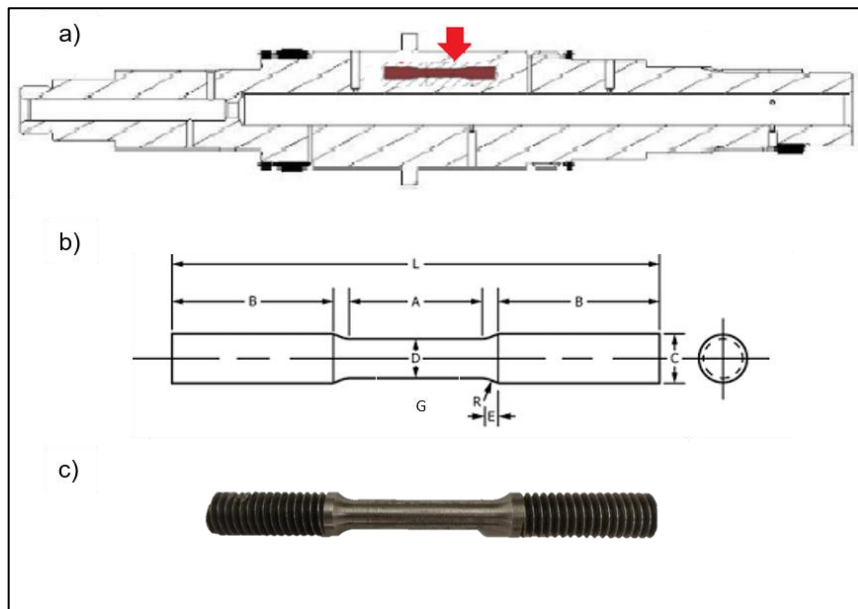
a) Localización probeta de tensión, b) Plano de probeta de tensión y c) Probeta de tensión maquinada
